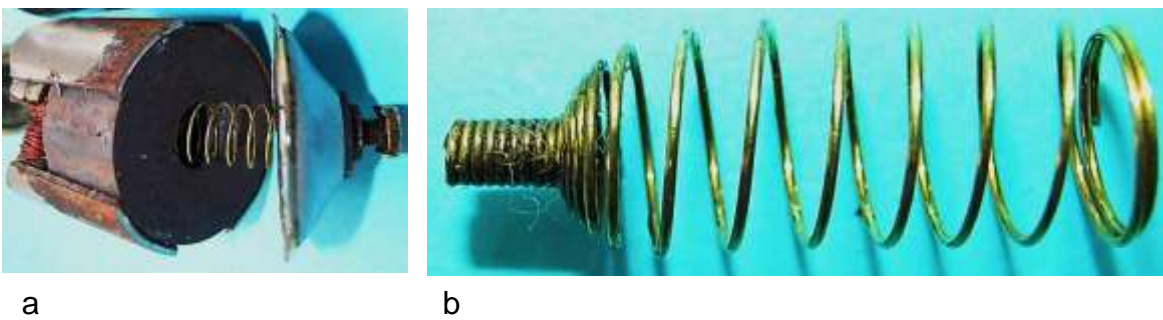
Federkontakt: a) Schleifkontakt innerhalb der Bohrung des Magneten, b) Kontaktfeder
